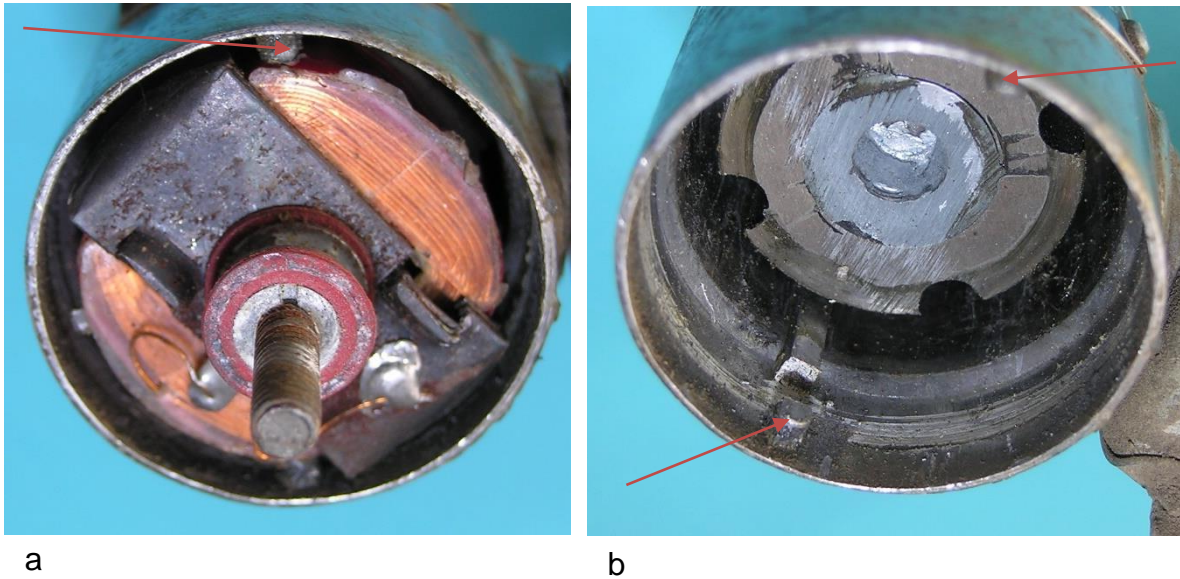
Gehäuseinnenraum: a) Anker, b) Polrad
